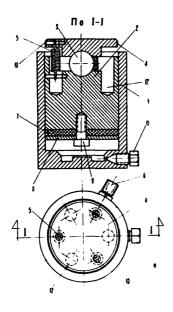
Схема гидродомкрата конструкции ВНИМИ грузоподъемностью 50 т с качающейся опорной площадкой:
